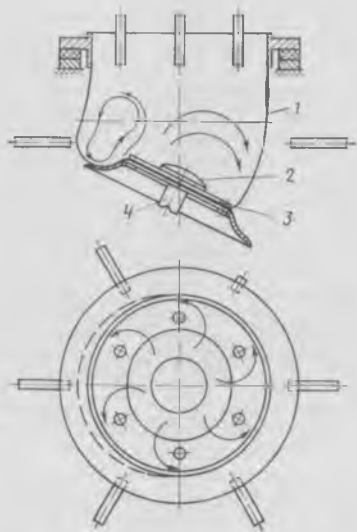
Схема безлопастного смесителя с гибким корпусом конструкции СПКО Оргтехстром
